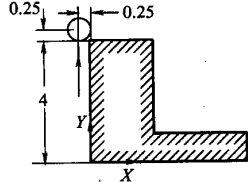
由直线组成轮廓铣削加工时的刀位点轨迹
